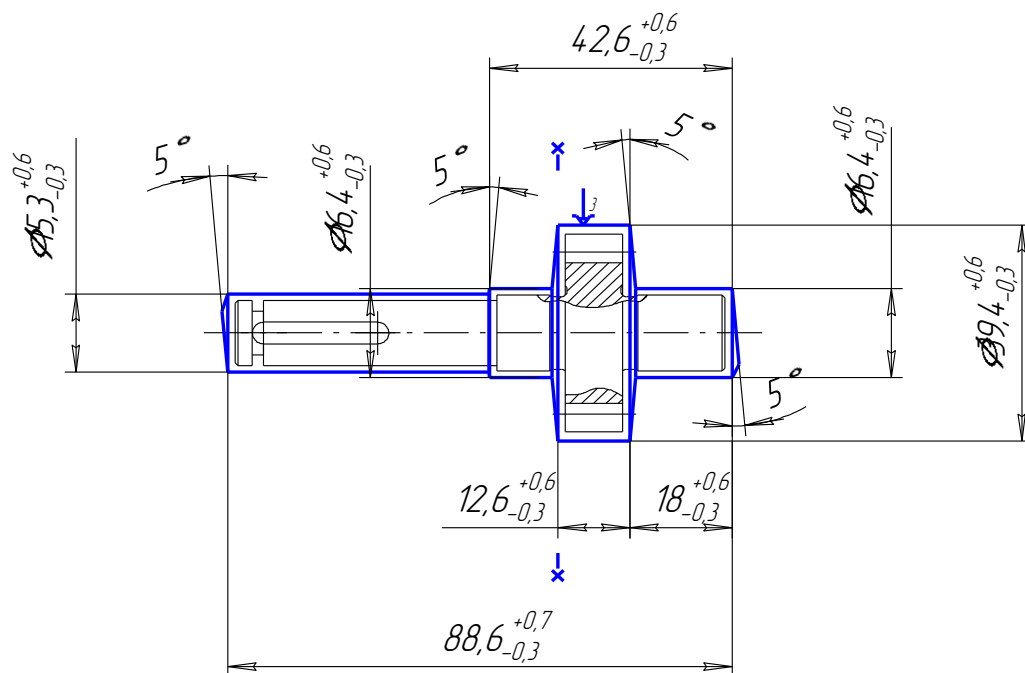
Ескіз заготовки поковки з уточненими розмірами
